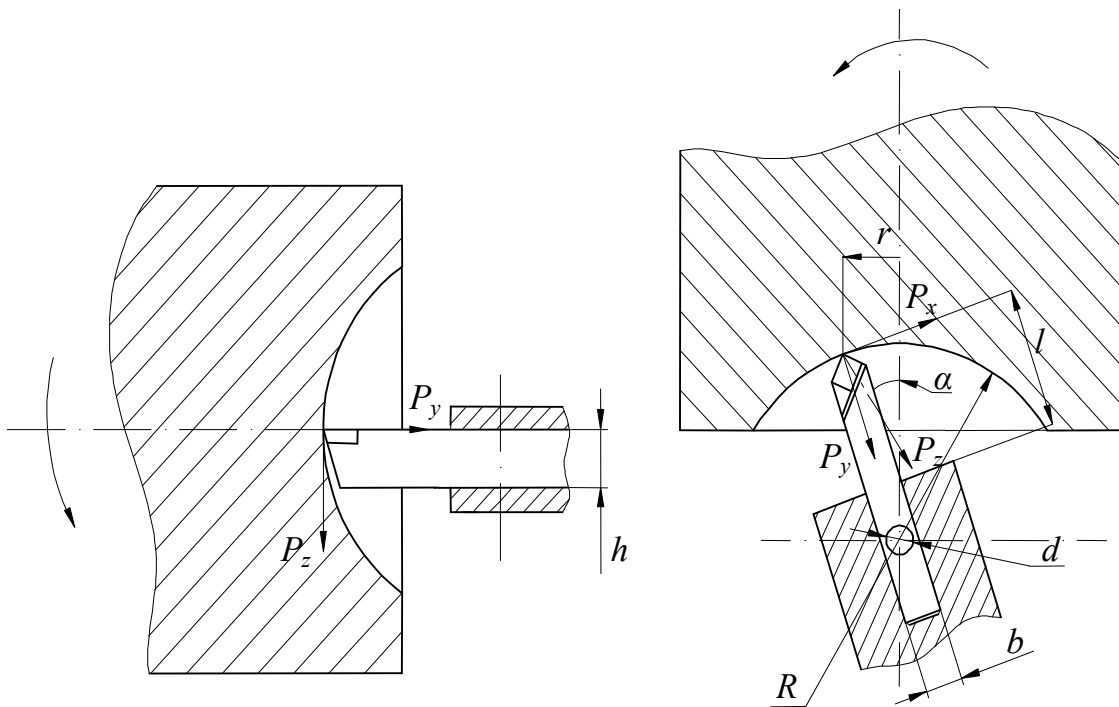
Розрахункова схема розточування сферичних поверхонь деталей машин
